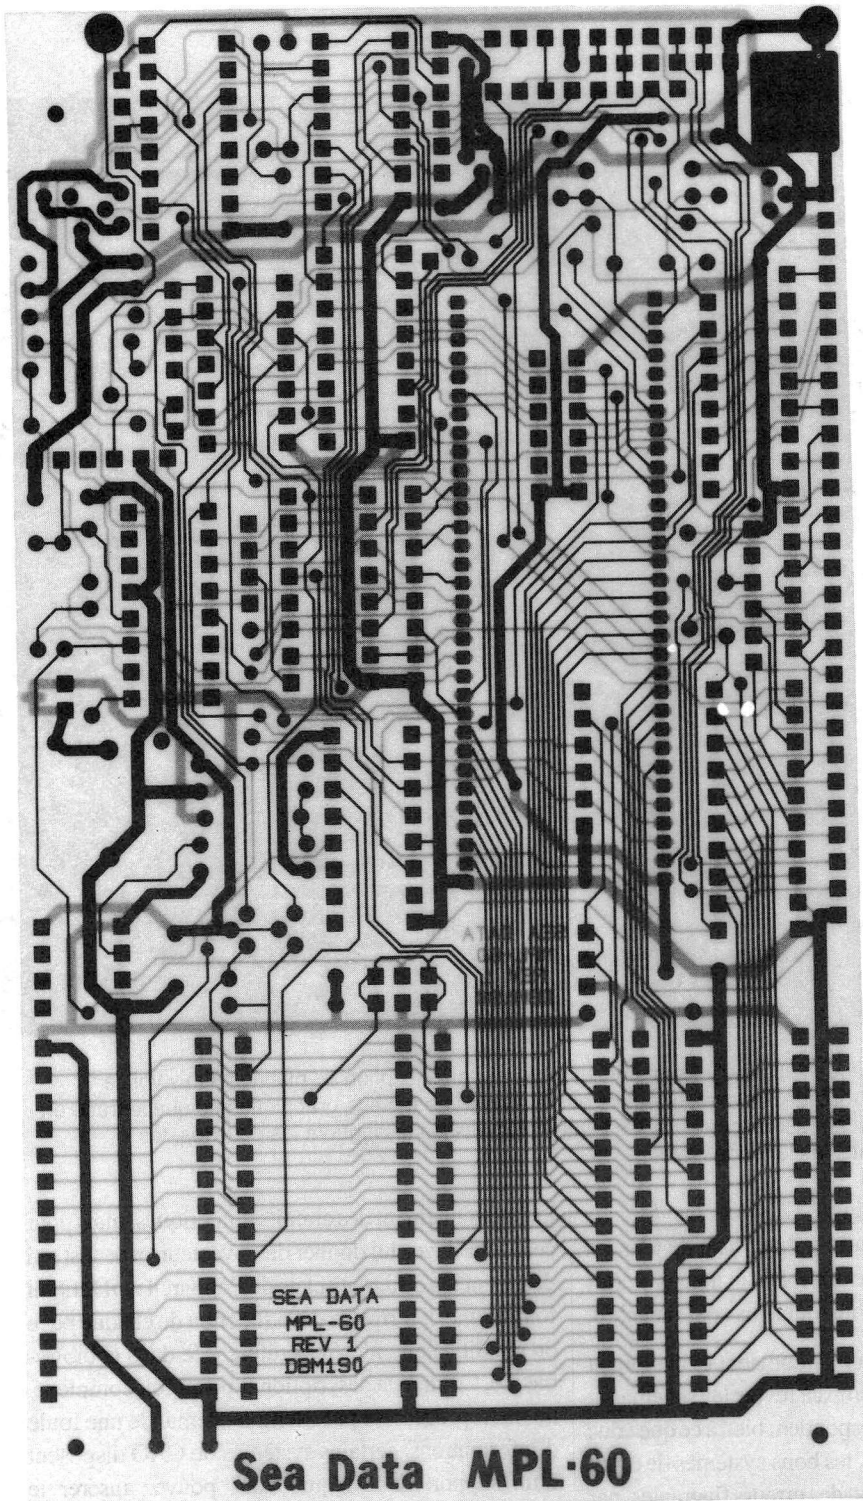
Relevé photographique du circuit de la platine à double face représentée à la figure 12.11. Les deux faces sont superposées sur cette photographie, le côté soudures en avant.
